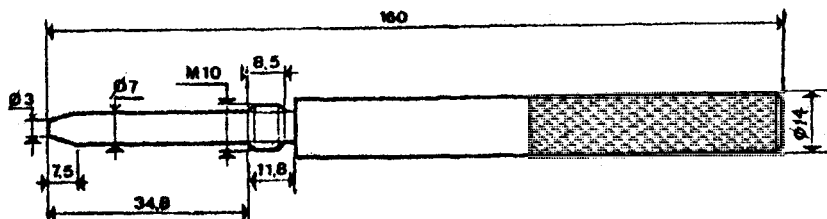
Приспособление для установки коленчатого вала в ВМТ
